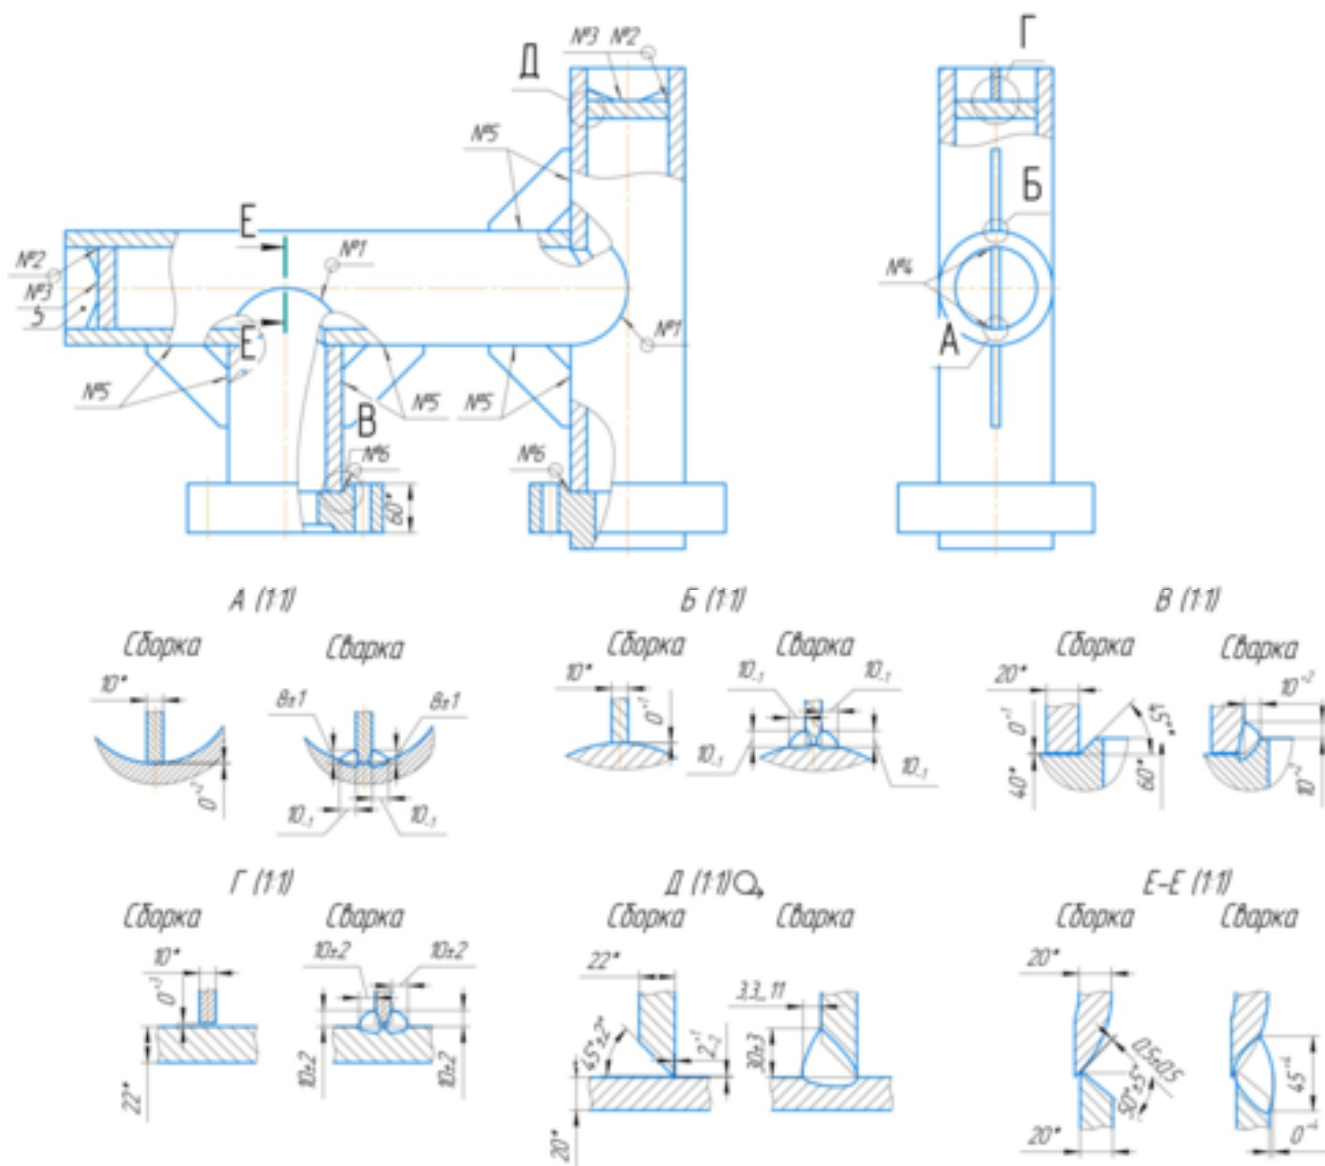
Схема расположения и вид сварных швов
